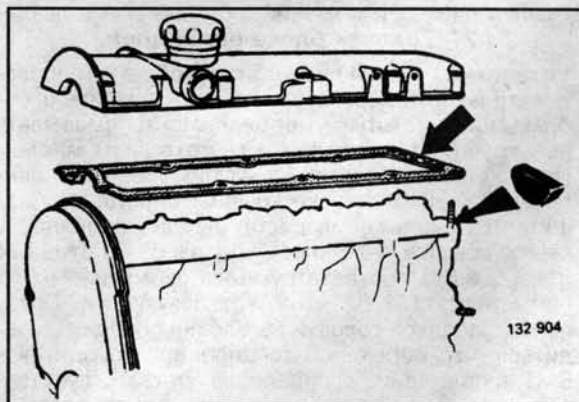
Прокладки под крышку распредвала двигателя В19
